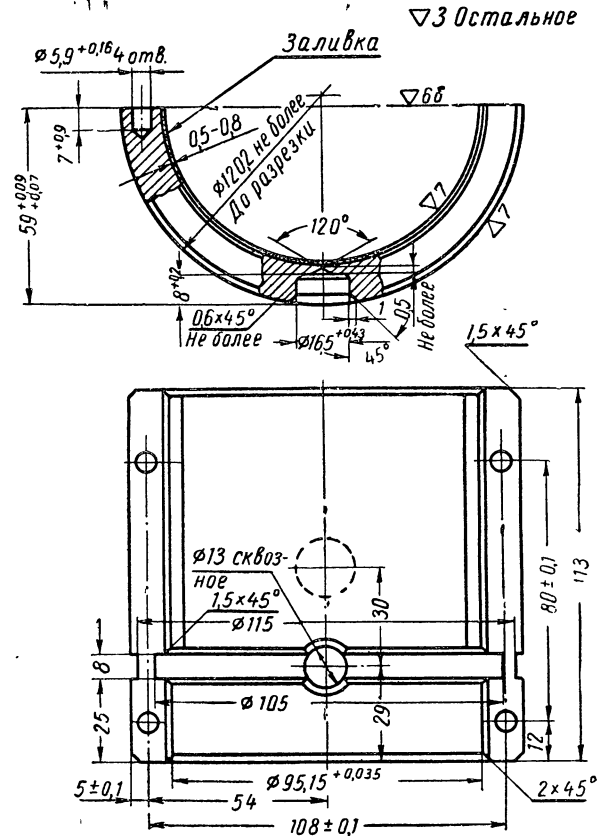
Нижний вкладыш заднего коренного подшипника.
